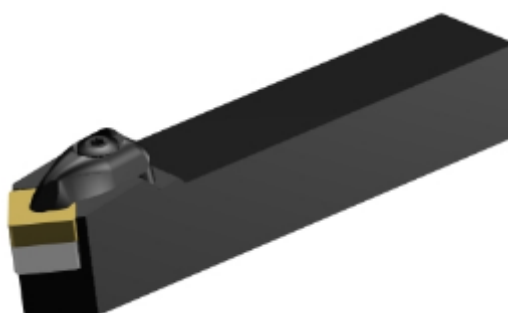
Маркування корпусу різця для напівчистої обробки DSDNN 2020K 12
